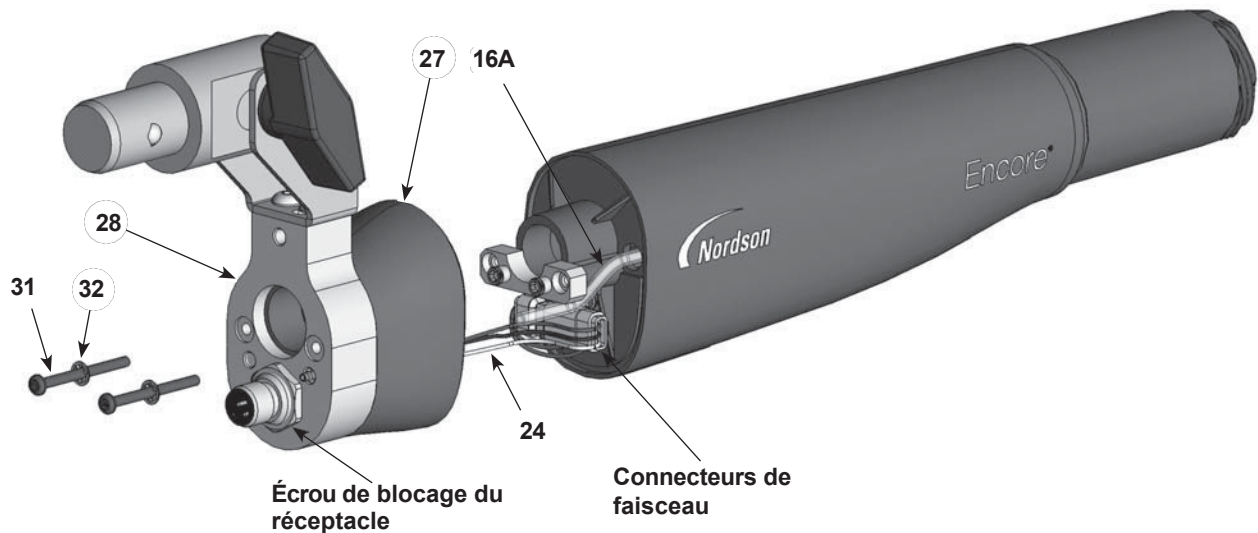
Démontage de l'embout du pistolet- Remplacement du tube de poudre
